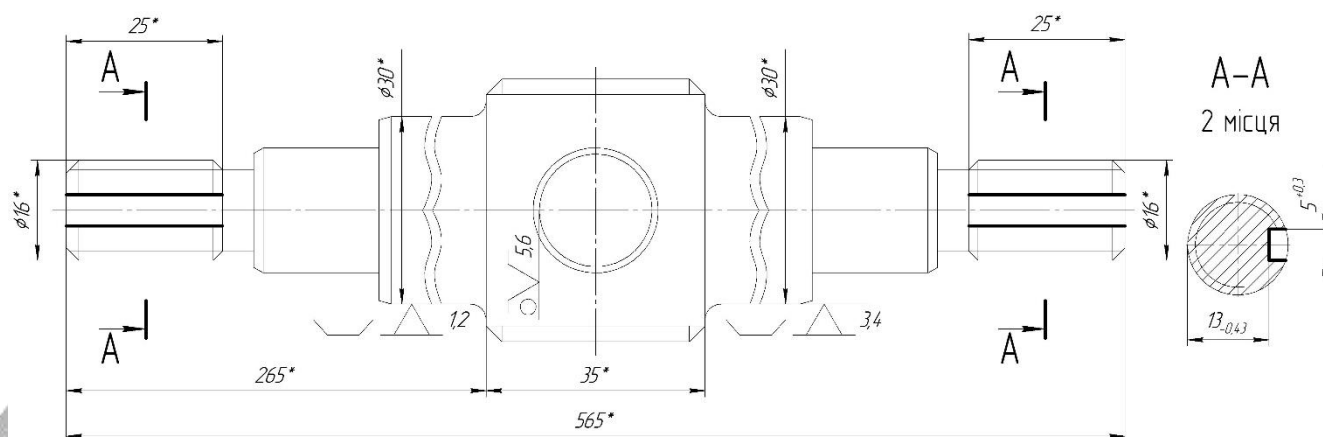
Схема базування заготовки на вертикально-фрезерній з ЧПК операції (другий варіант)
